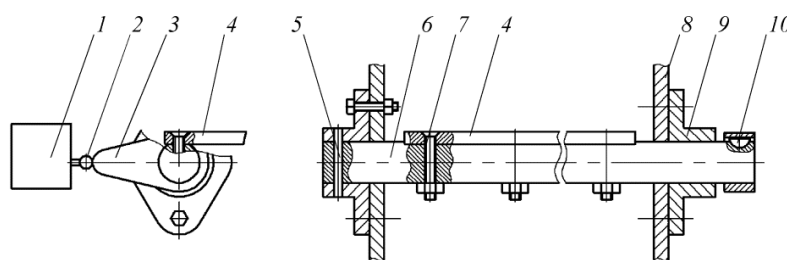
Схема конструкции защитного устройства противорежущей пластины:
